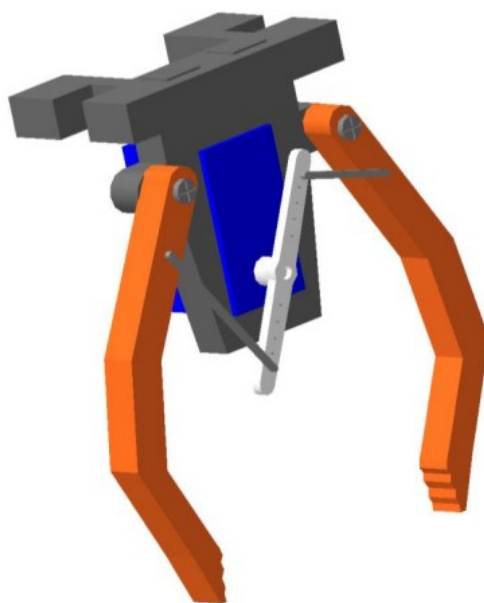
3D-модель обраного захватного пристрою
